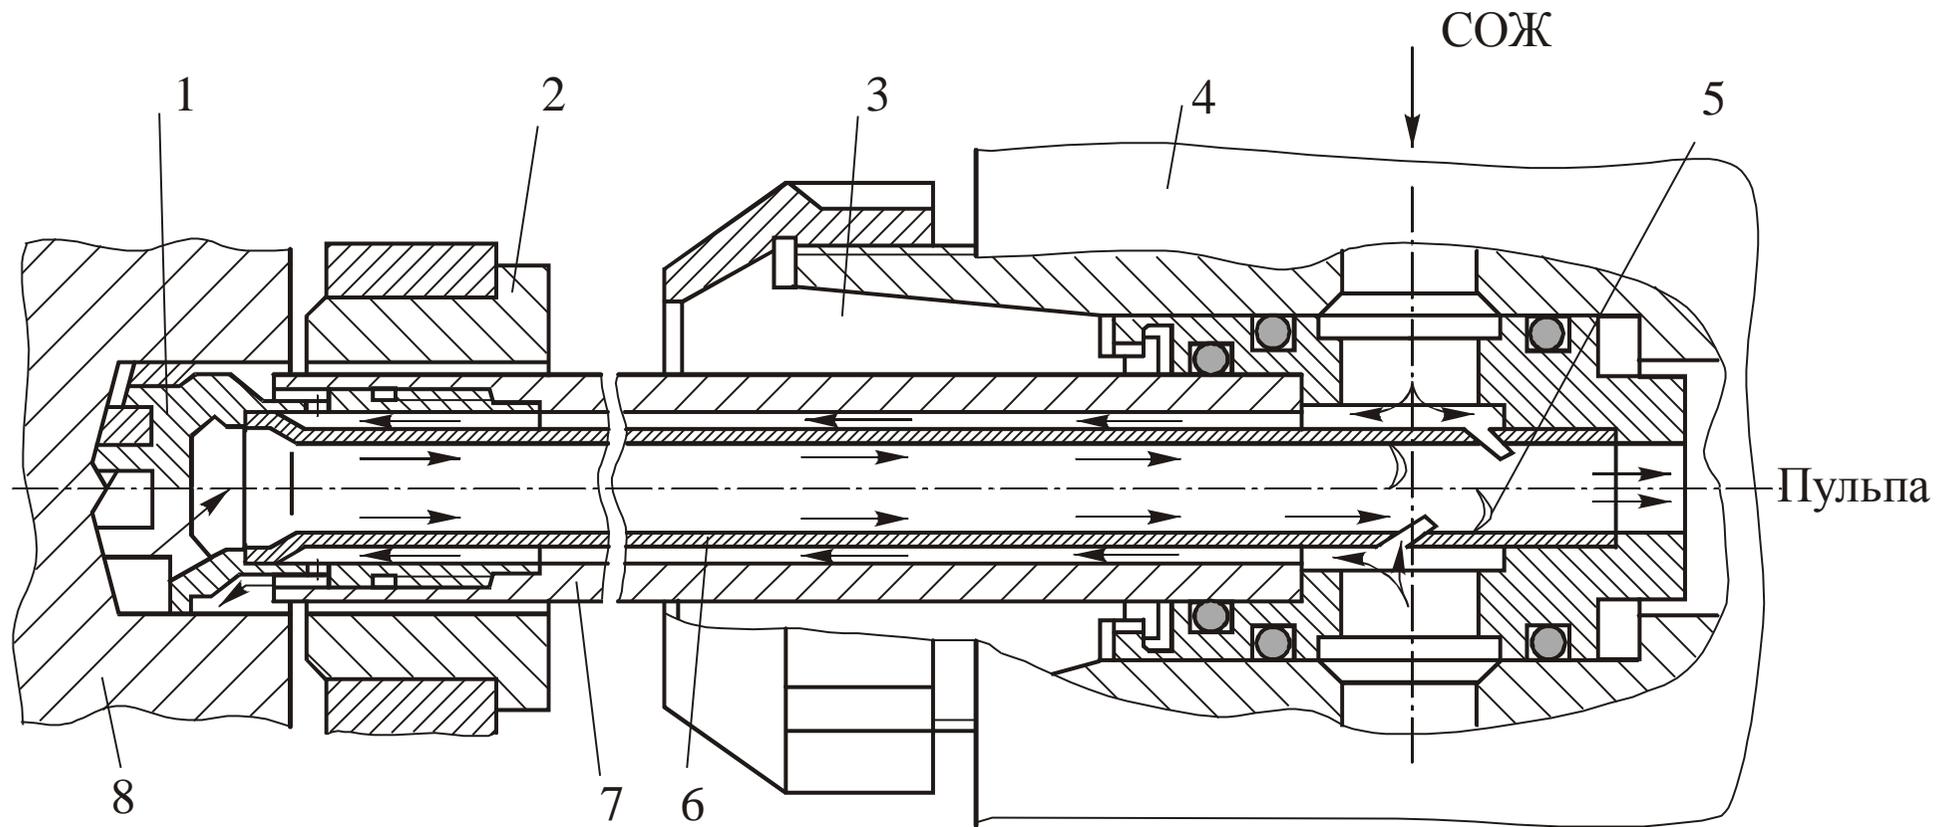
Схема работы эжекторного сверла: 1 – режущая головка; 2 – кондукторная втулка; 3 – цанга; 4 – зажимной патрон; 5 – сопла эжектора; 6 – тонкостенная труба; 7 – стембель; 8 – заготовка
